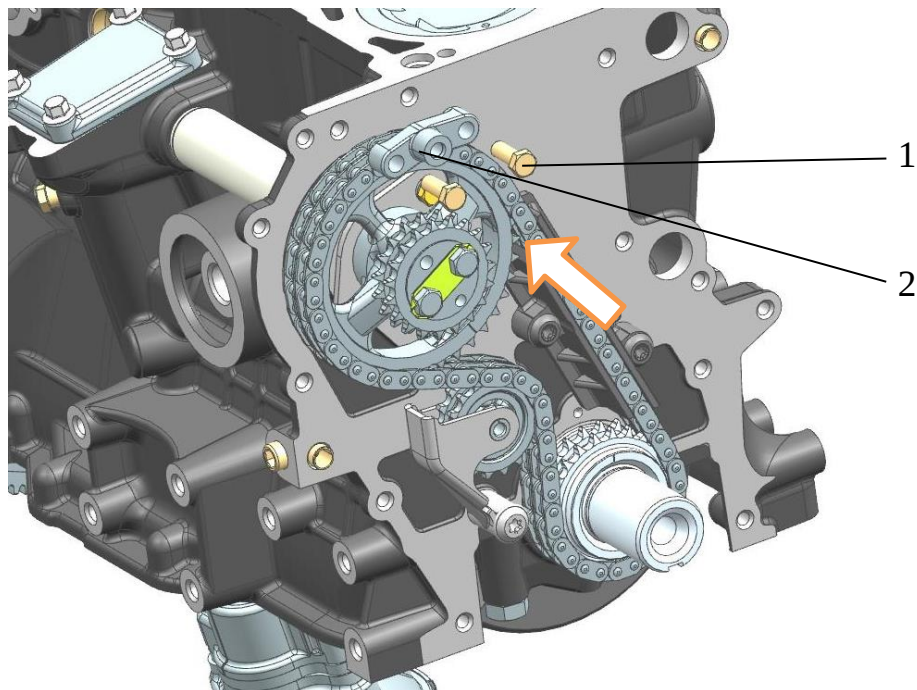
Установка опоры верхнего рычага натяжного устройства:
